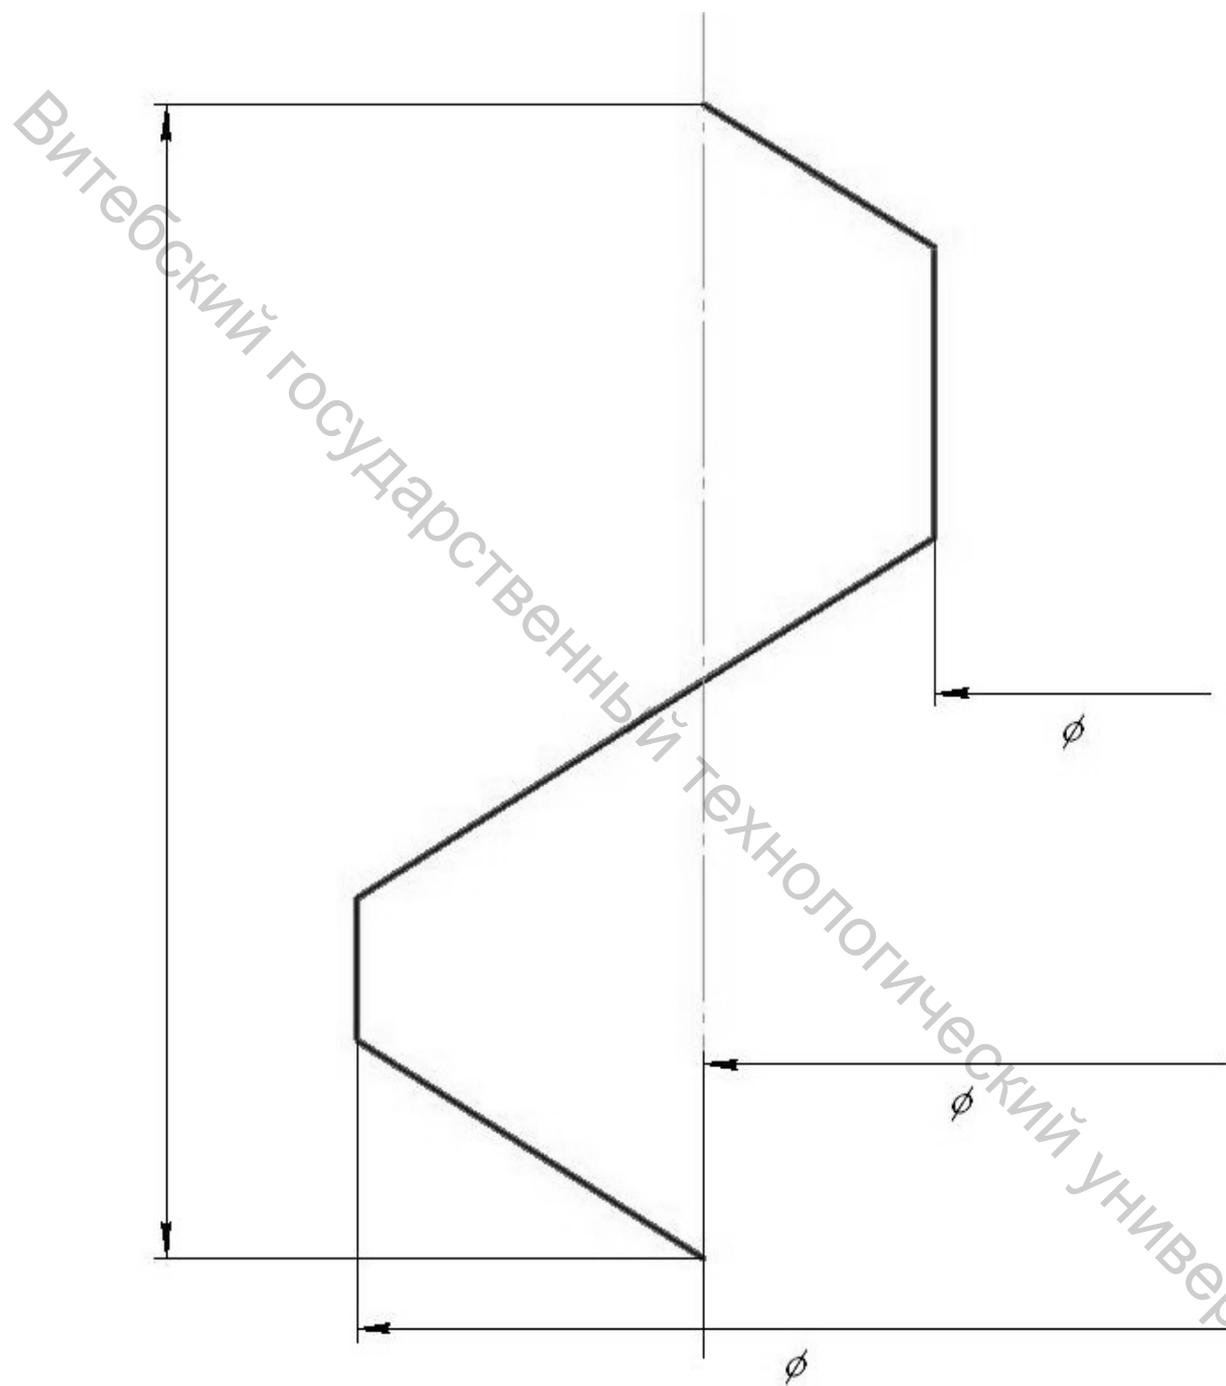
Схема расположения интервалов допусков резьбовой посадки М \_\_\_\_\_ - -----
